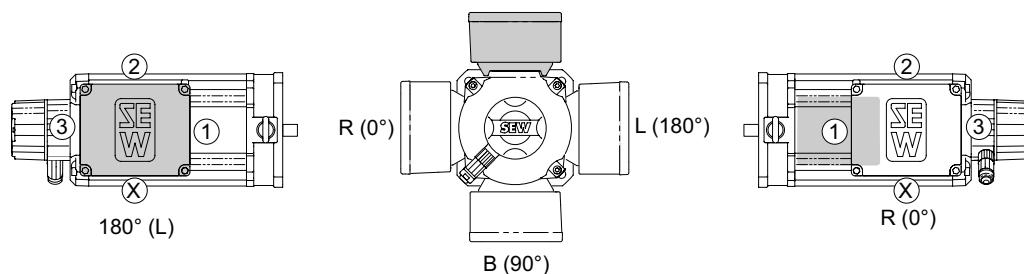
Lage des Klemmenkastens und der Kabeleinführung
